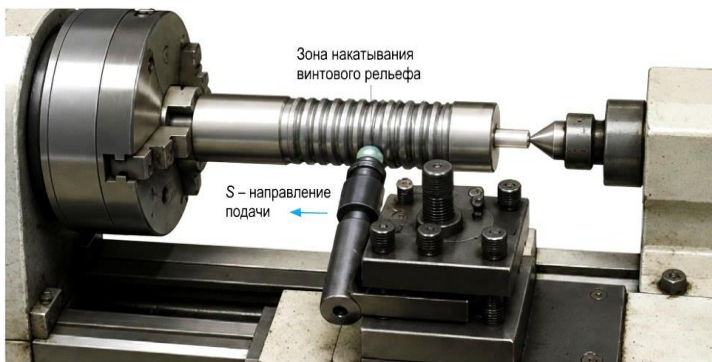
Токарный станок с установкой инструмента и деталью.
